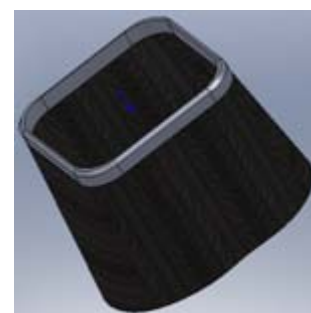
Устройство юбки, прикрепляющейся к корпусу бокса
